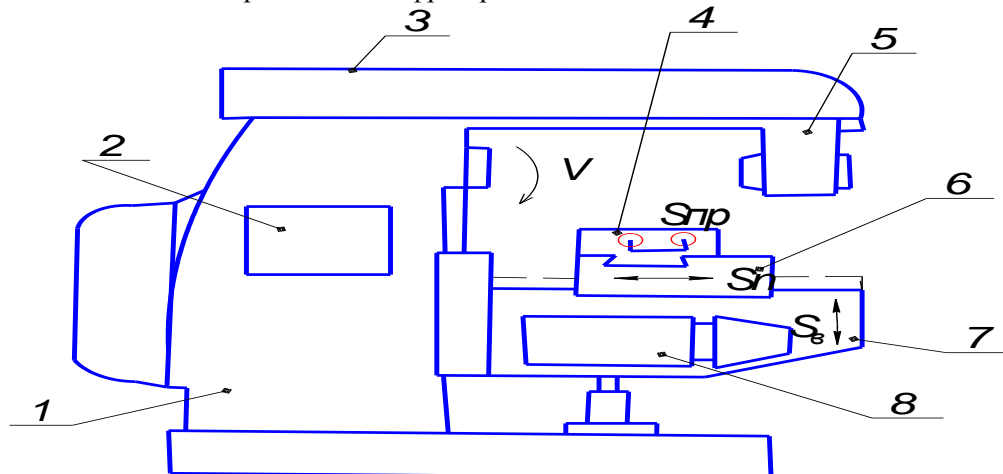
Общий вид консольного горизонтально-фрезерного станка 6P82Г
